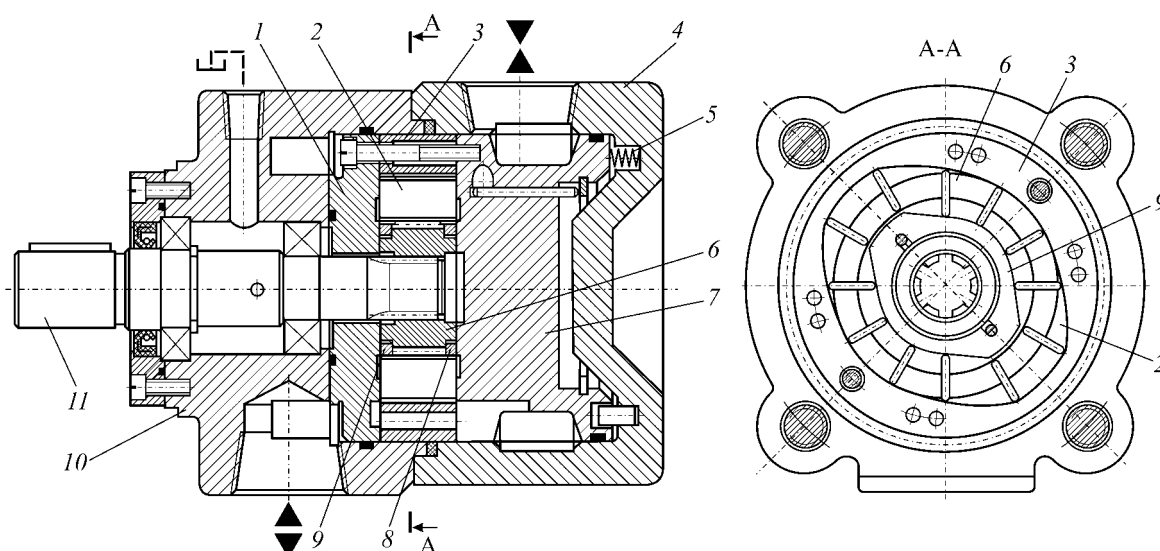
Пластиначный гидромотор серии МГ16-1: 1, 7 – передний и задний диски; 2 – пластины; 3 – статор; 4 – задняя крышка; 5 – пружина; 6 – ротор; 8, 9 – кулачки; 10 – корпус; 11 – вал
